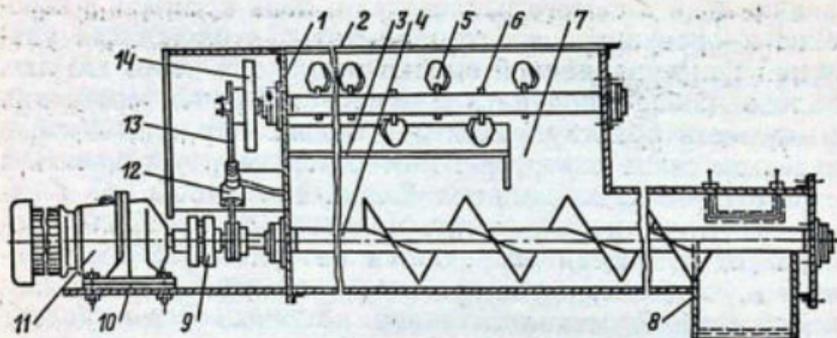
Шнековый извлекатель КПГ-10.46.03:
